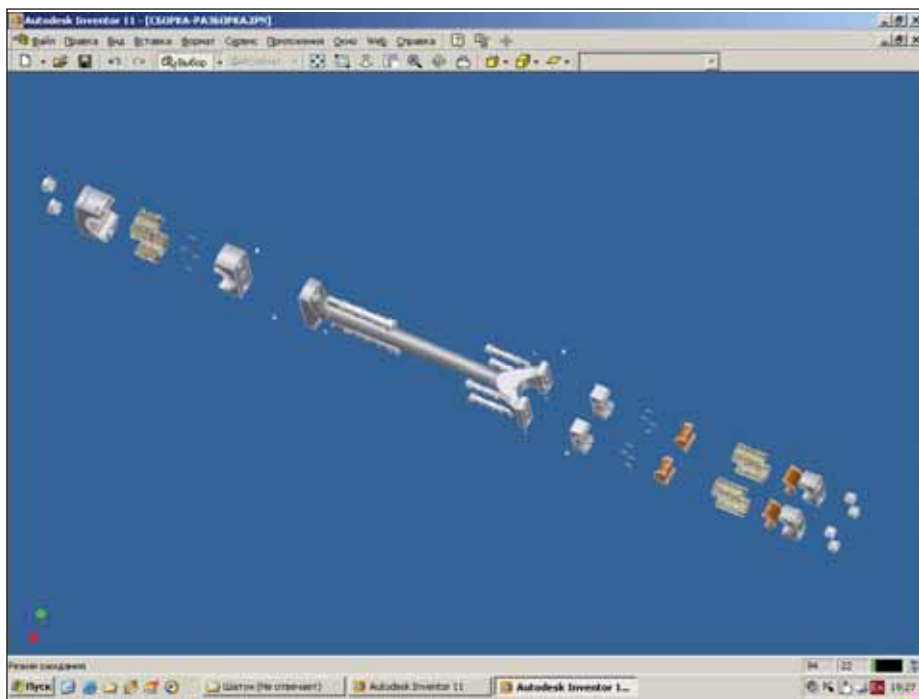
3D-модель сборки-разборки шатуна, выполненная в Autodesk Inventor
